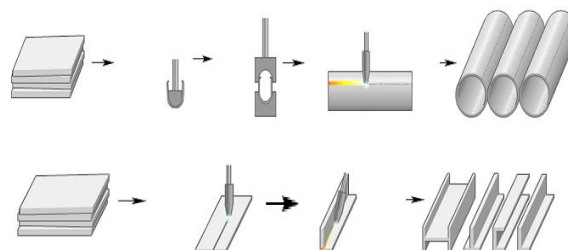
Schema generale di trasformazione delle lamiere in tubi e sezioni (Steeluniversity.org)
